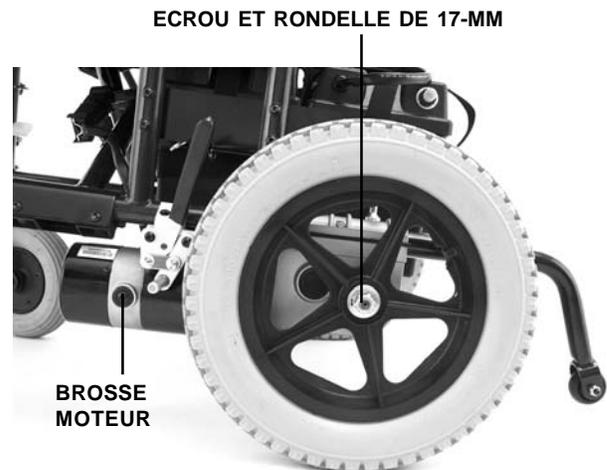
Emplacement écrou de roue et couvercle de brosse de moteur
